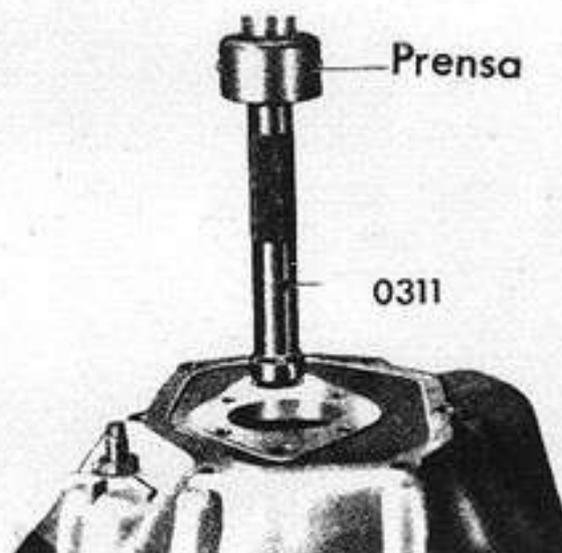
Montaje del cojinete de agujas del quintuple en la cubierta de embrague
